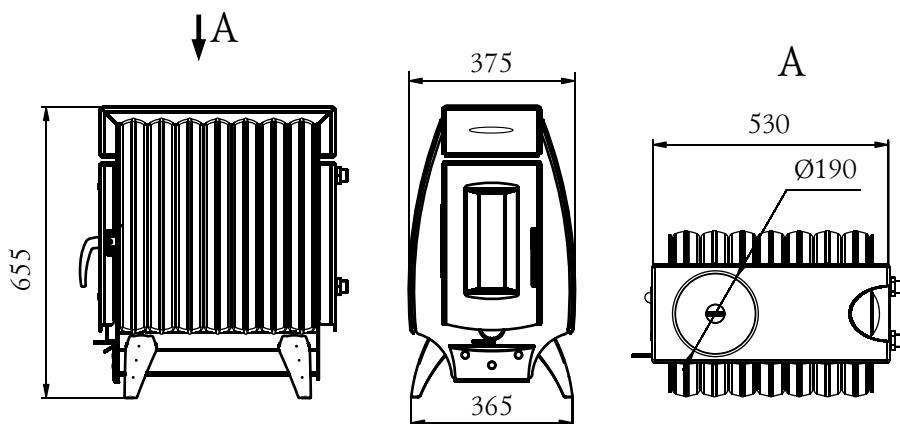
Габаритные размеры печи «Огонь-батарея 7Б».
